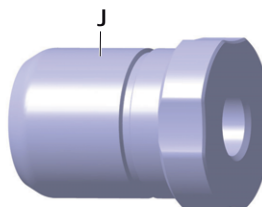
Переходная гильза для утверждения/проверки при помощи калибровочной матрицы для инструментов Brainlab, версия 4
